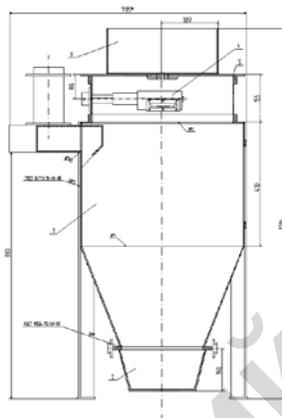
Установка получения металлических порошков распылением расплава металла воздухом:
